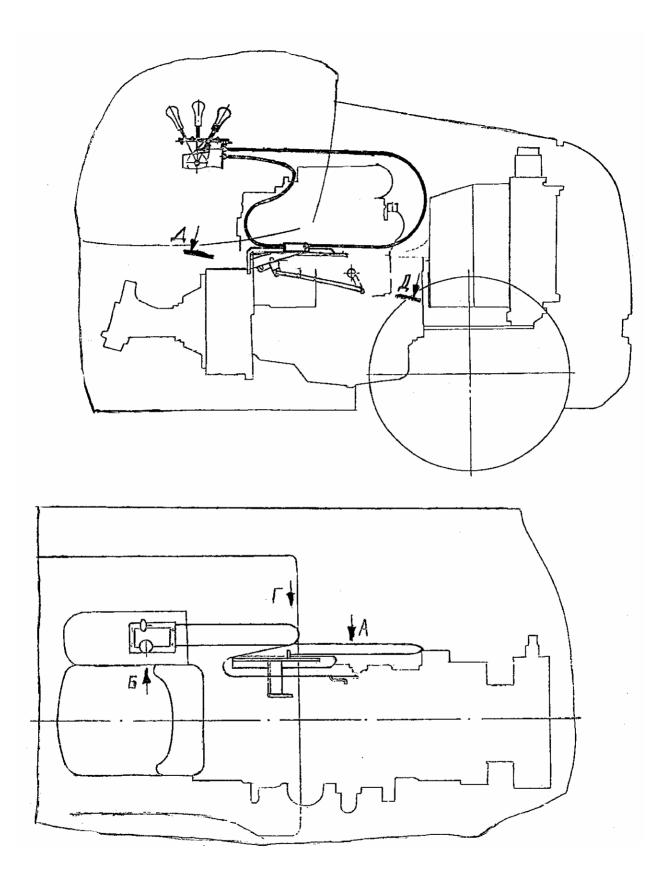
Управление двигателем Fig. 45.1 Engine Control System
